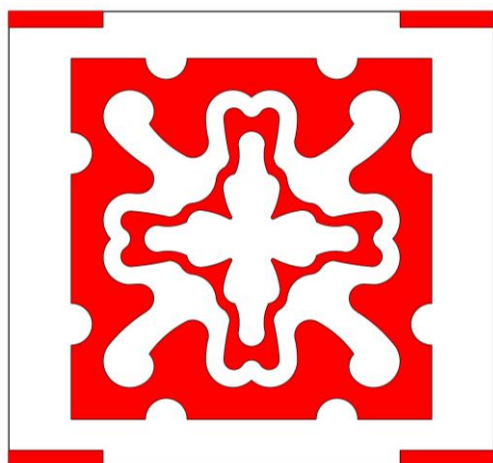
Percentagem de desperdício material _ Fonte: desenho técnico da autora
